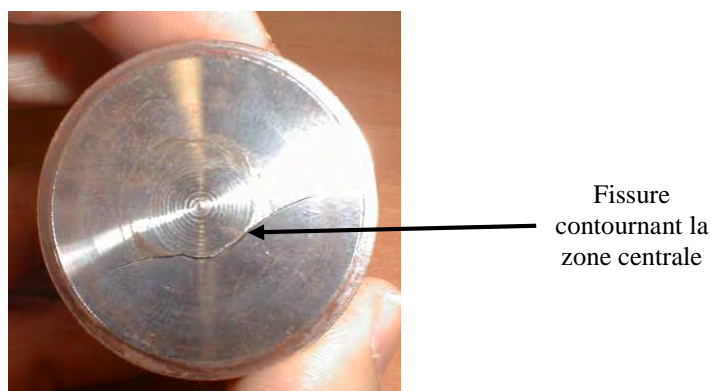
Fissure typique sur la face extérieure du poussoir usiné
